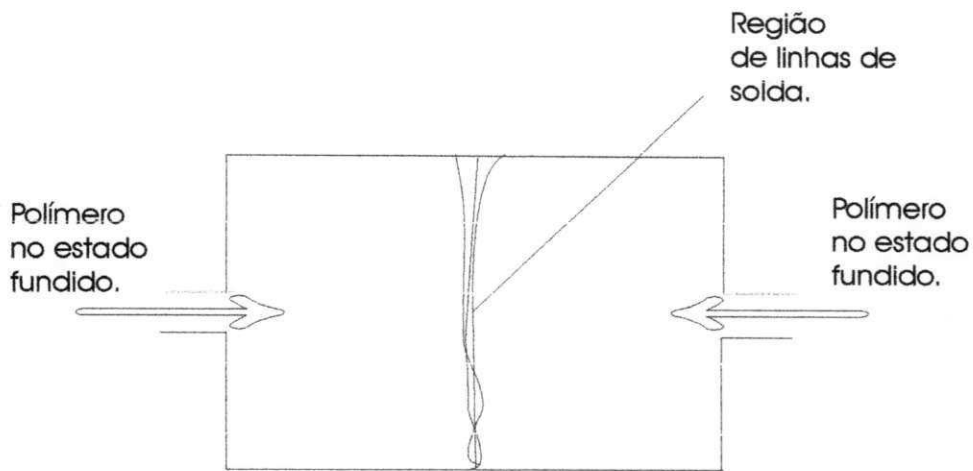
Linhas de solda em um tubo obtido por extrusão.
